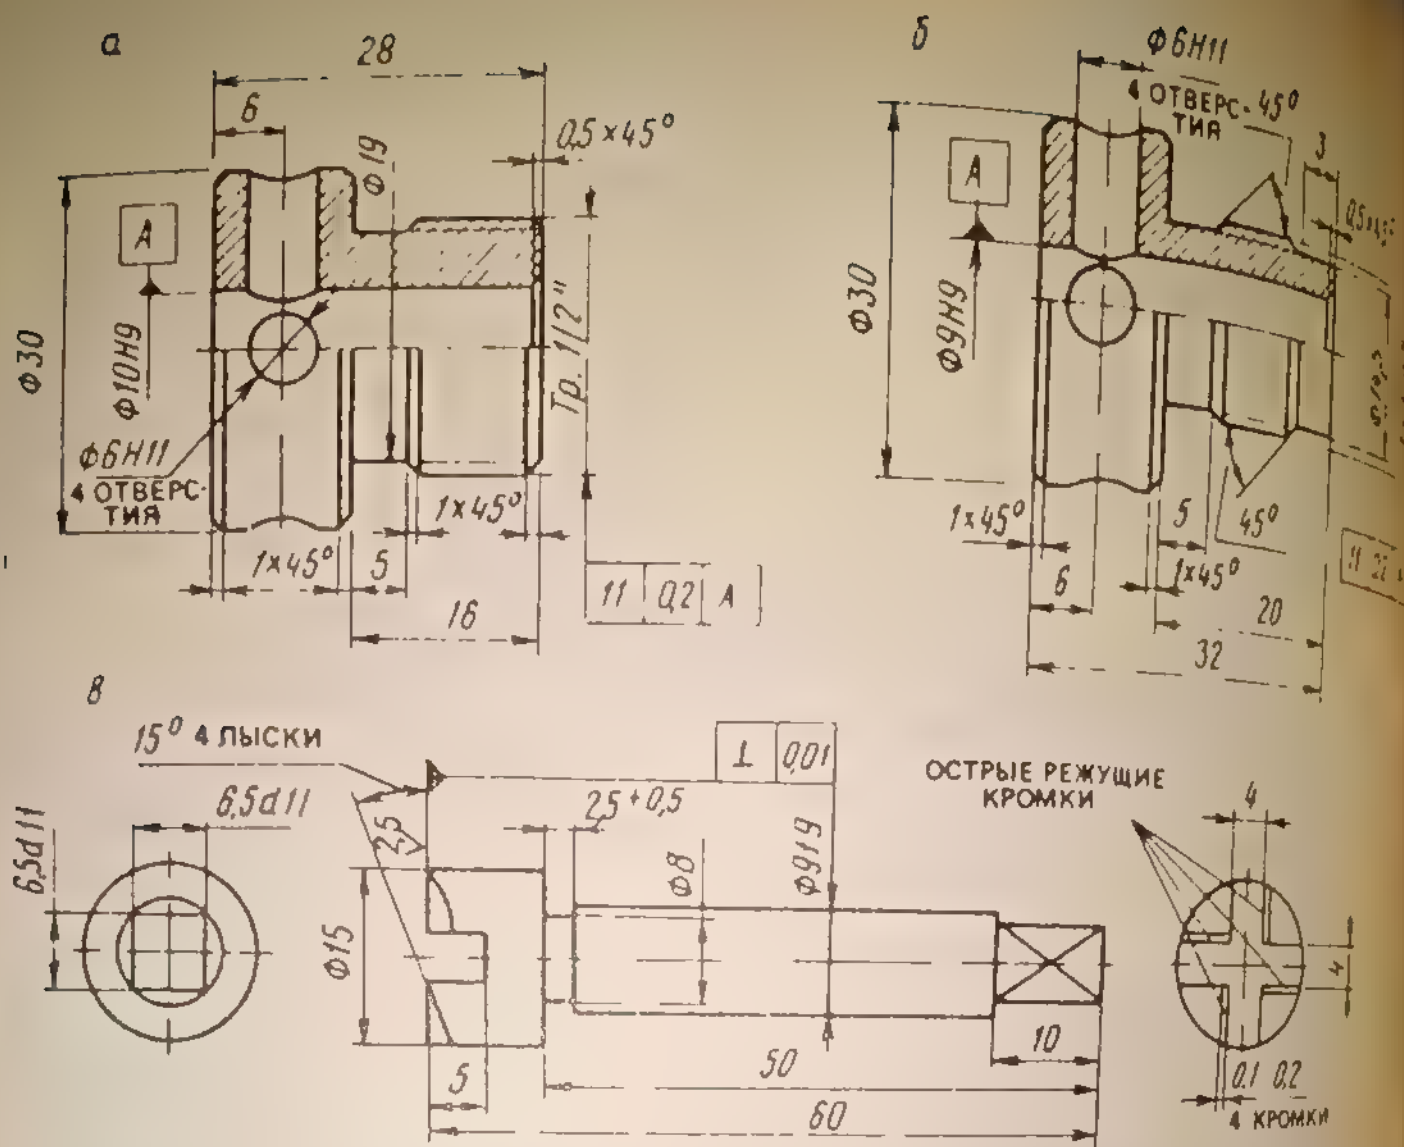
Детали приспособления для фрезерования седел вентиля зару-
